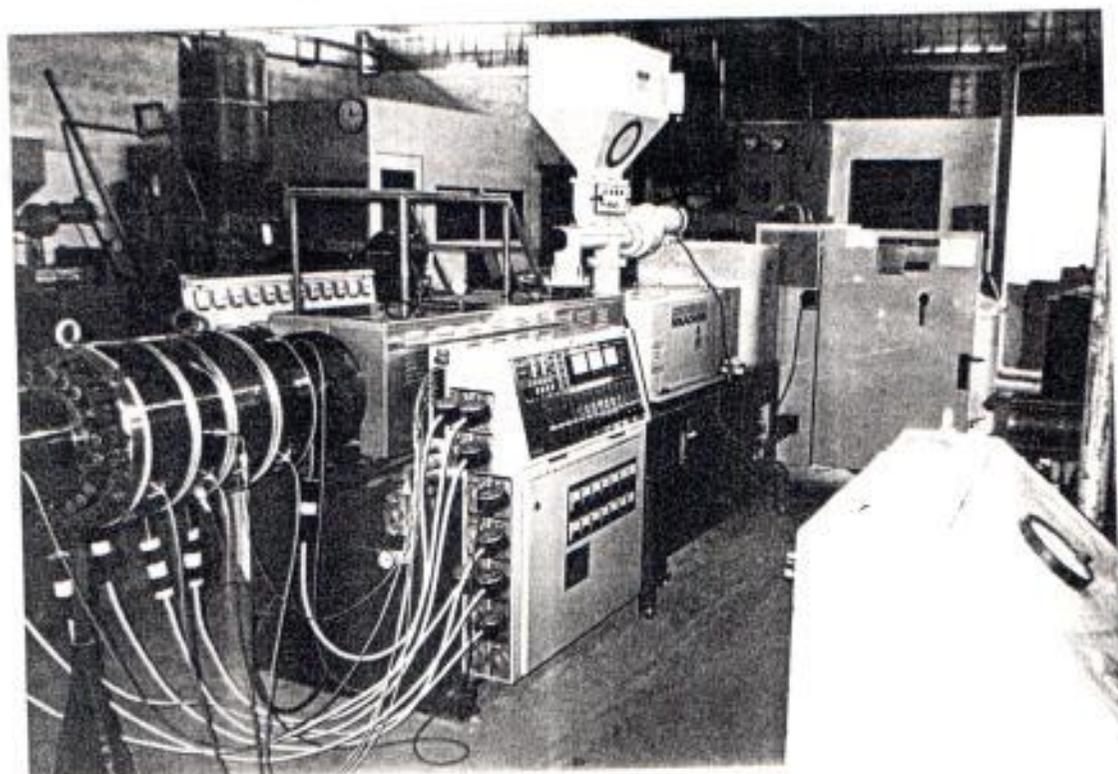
VISTA PRINCIPAL DE LA MAQUINA EXTRUSORA.
